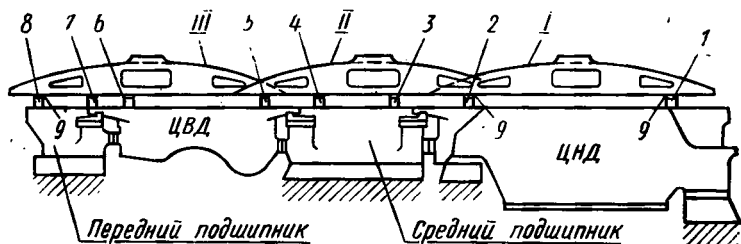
Схема центровки двухцилиндровой турбины по уровню
